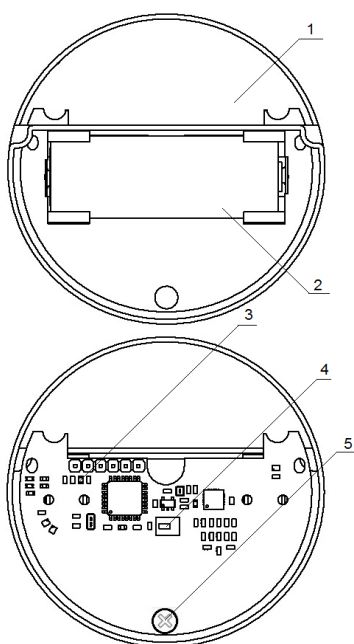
Внешний вид счетчика с модулем (вид сверху)
